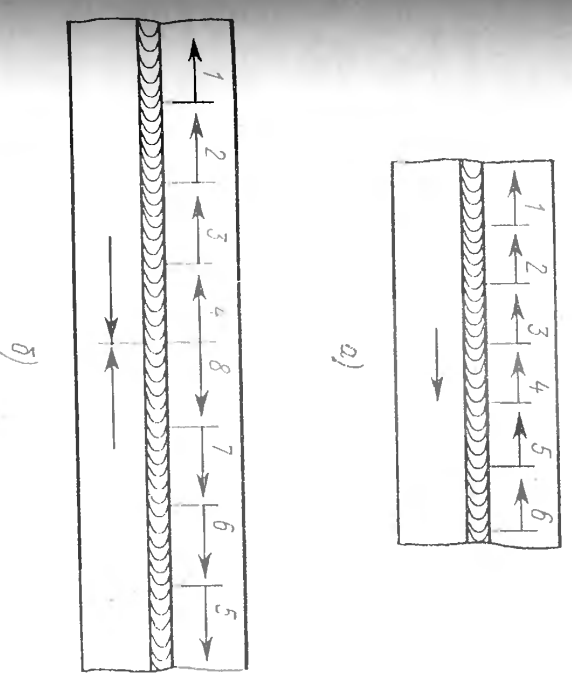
Последовательность (1...8) наложения не-больших (а) и длинных (б) швов при обратноступенчатом способе сварки
